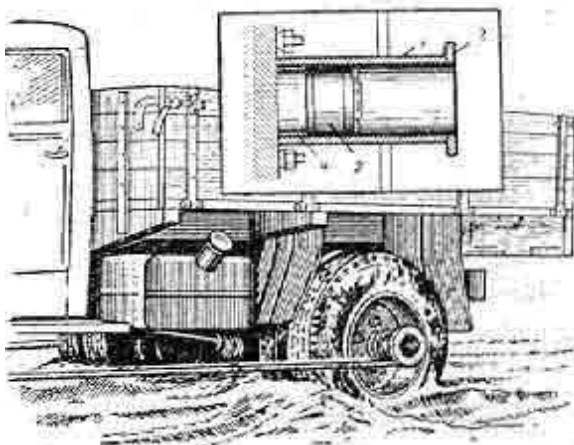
Схема устройства и применения самовытаскивателя. 1- барабан; 2 - фланец; 3 - ступица 4 - накладка.
